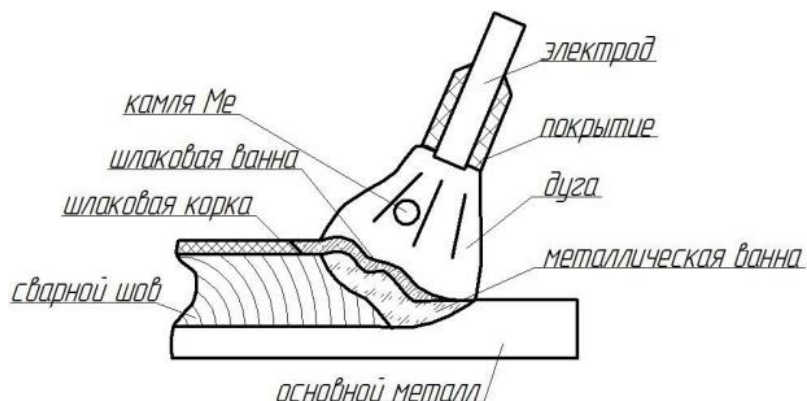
Схема выполнения ручной дуговой сварки
